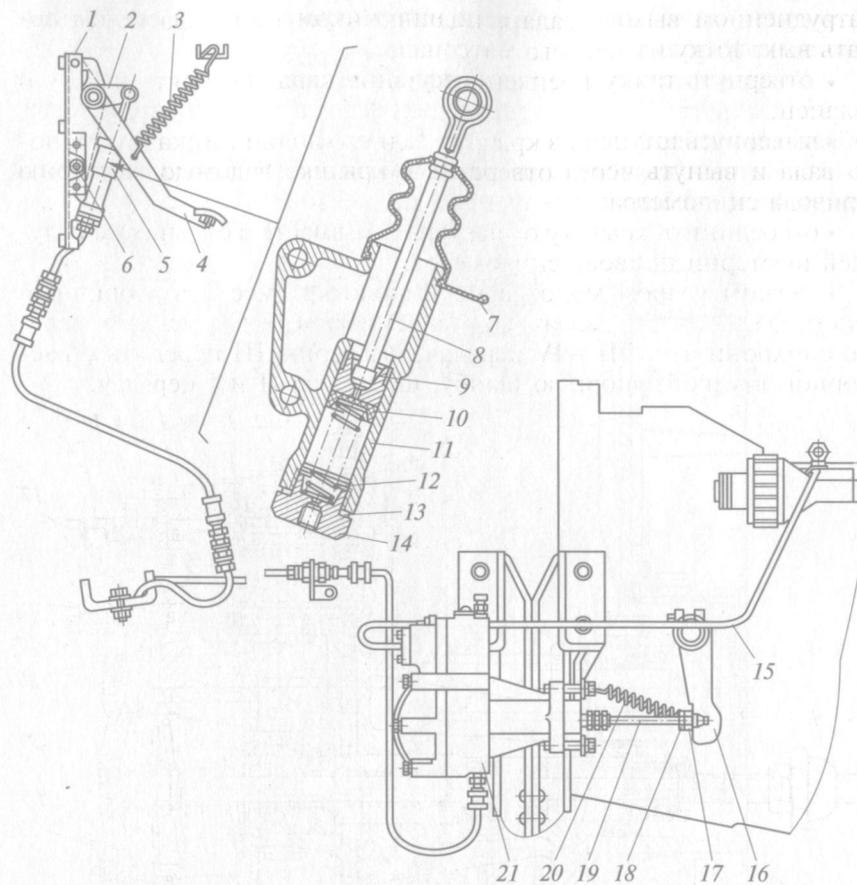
Гидравлический привод сцепления в автомобилях семейства КамАЗ:
